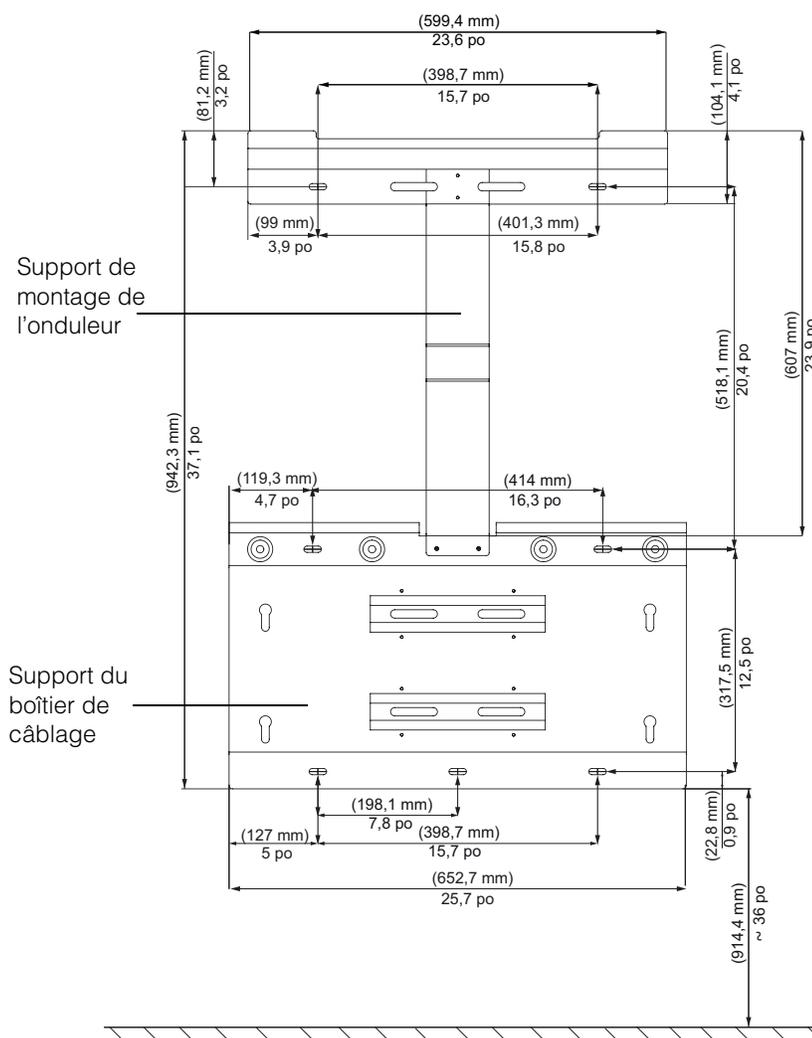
Dimensions des supports de montage – Boîtier de câblage et onduleur
